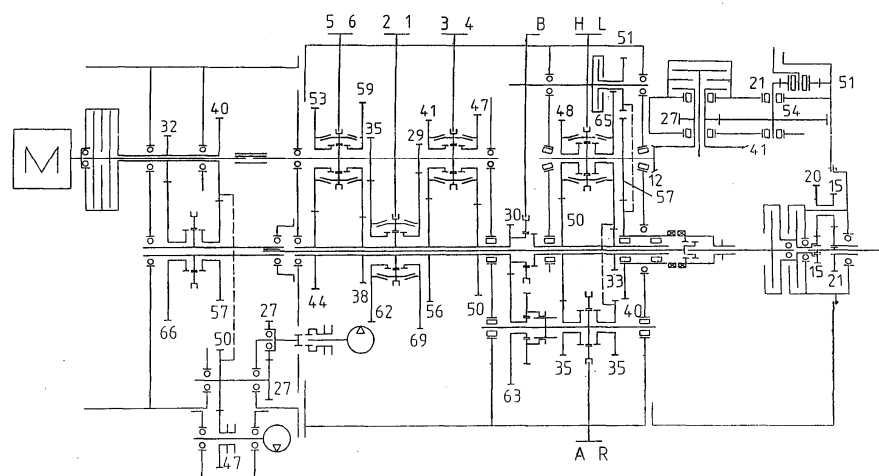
Кинематическая схема опытной коробки передач с двухпарным зацеплением
